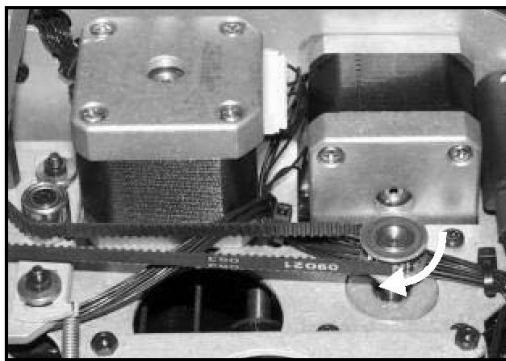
поверните привод двигателя блока фокусировки до предельного положения в поступательном направлении
